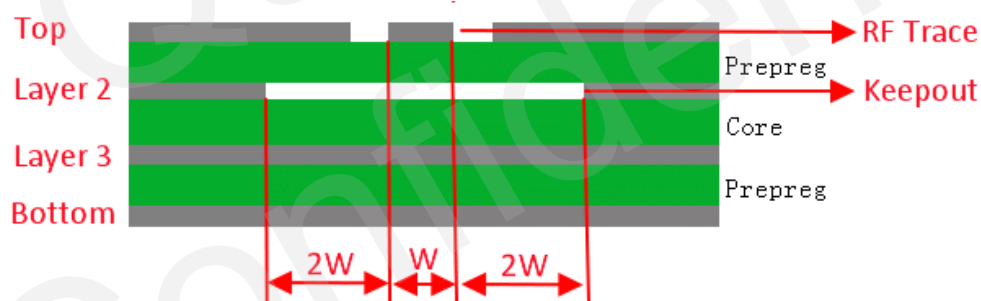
：四层板 LAYOUT 示意图(参考地是第三层)
